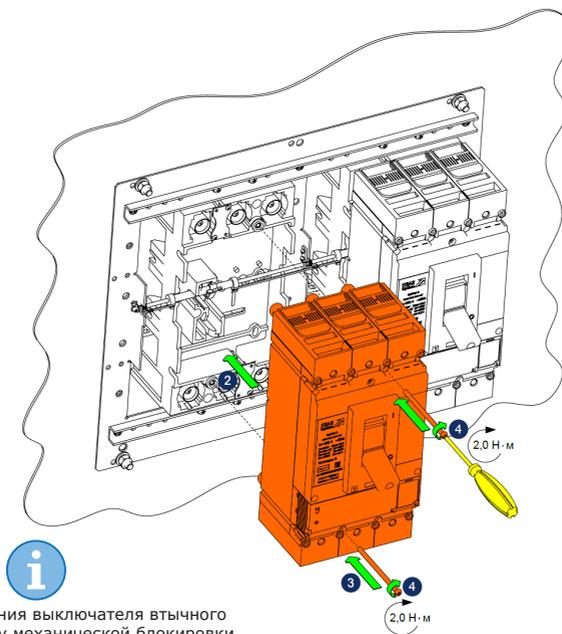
Установка толкателя блокировки на стационарный выключатель
